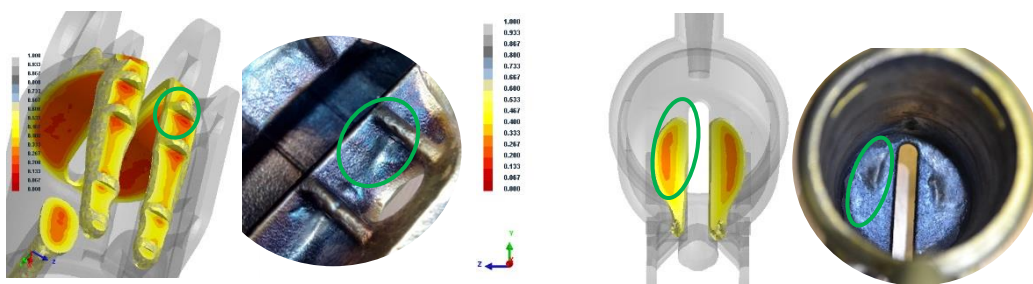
Zobrazení CutOff – oddělení tekuté fáze od odlitku
